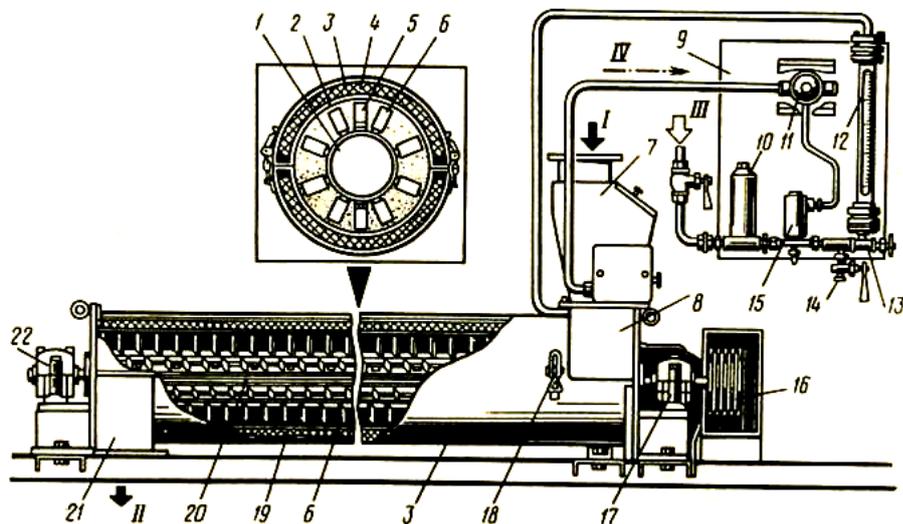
Машина А1-БШУ-2 для зволоження зерна: 1 – вал; 2 – корпус; 3 – кожух; 4 – прокладка; 5, 6 – лопаті; 7 – індикатор наявності зерна; 8, 21 – приймальний і випускний патрубки; 9 – панель; 10 – фільтр; 11 – електророзетка; 12 – ротаметр; 13 – голчастий вентиль; 14 – зливний кран; 15 – електромагнітний вентиль; 16 – привід; 17, 22 – корпуси підшипників; 18 – запірний механізм; 19 – бич; 20 – шпилька.
